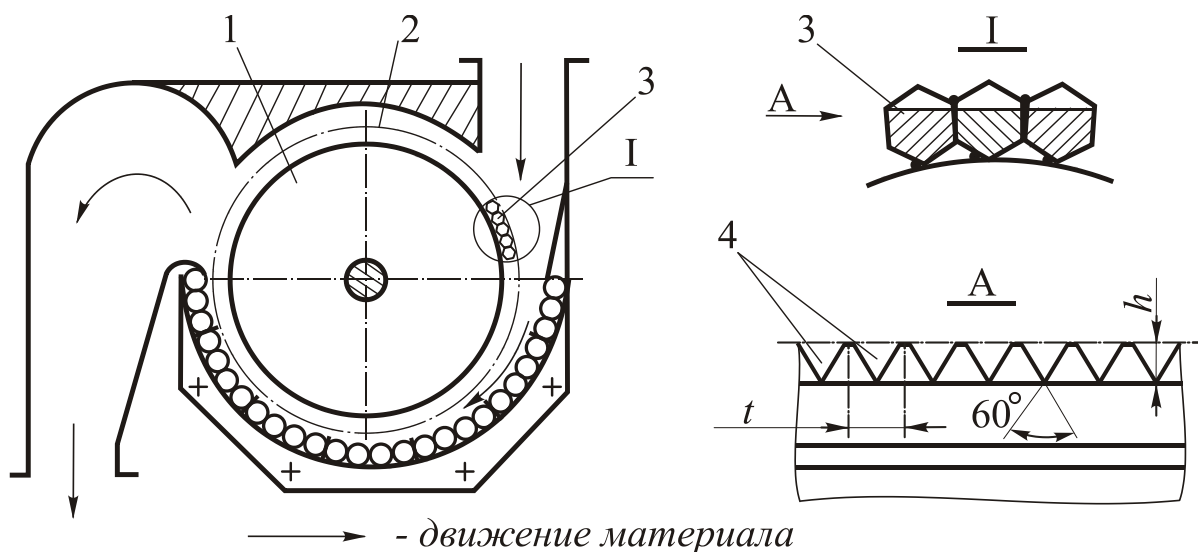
Схема работы устройства клеверотерки-скарификатора КС-0,2 с усовершенствованной конструкцией барабана: 1 – барабан; 2 – терочная поверхность барабана; 3 – стальные прутки из шестигранника; 4 – поперечные канавки
